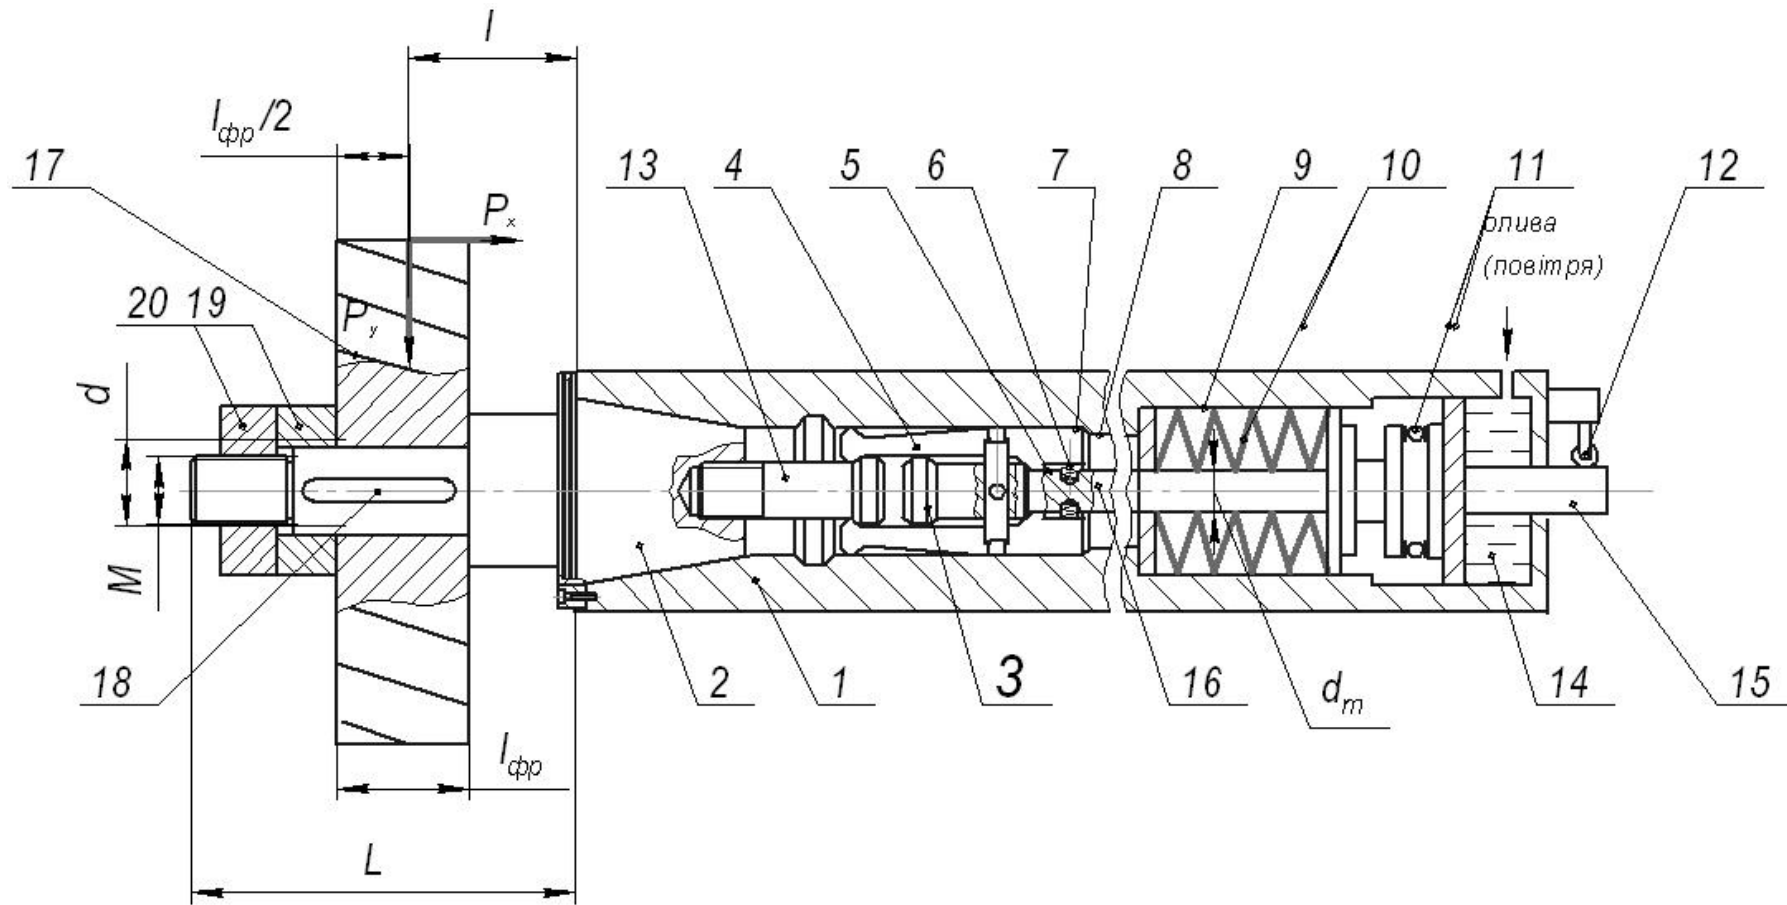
Закріплення дискової фрези на багатоопераційному верстаті
